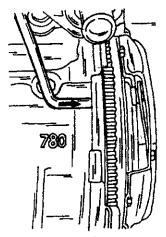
Стержень для блокировки коленчатого вала вставляется с задней стороны картера двигателя в указанном месте.
